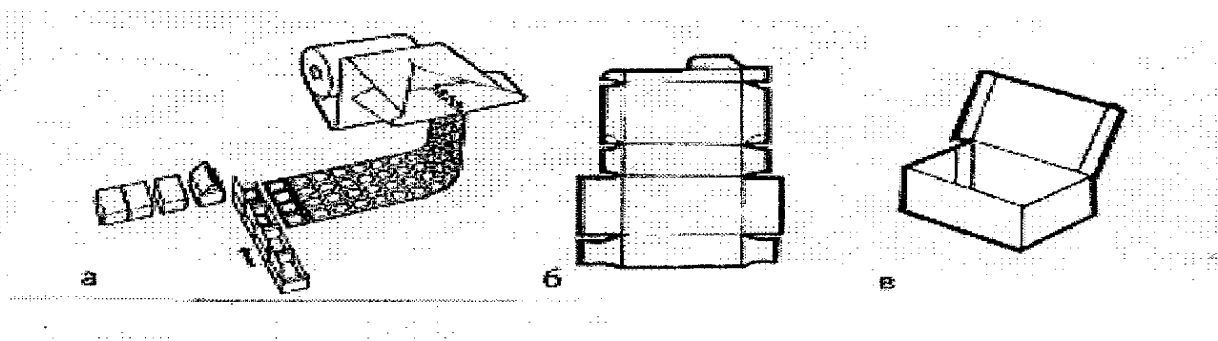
Схема укладання продукції в тару, яка отримана з штампованої заготовки: а- схема процесу; б-штампована заготовка картонної коробки; в- зібрана коробка
